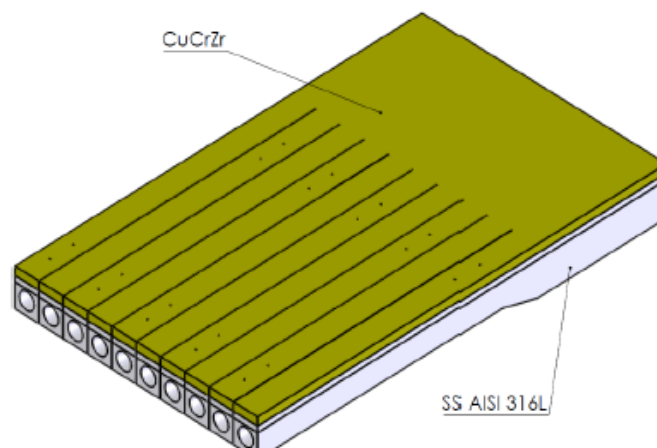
Geometría tras la segunda simplificación del panel first wall.
